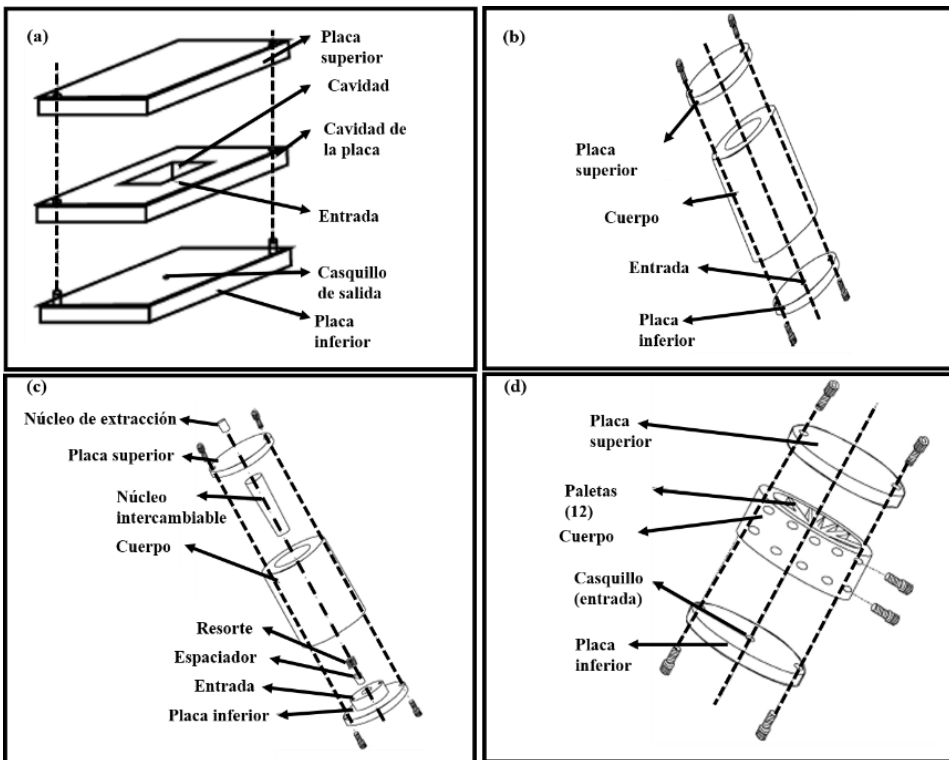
Moldes utilizados en el moldeo por inyección de polvos a baja presión, (a) molde para barras, (b) molde para cilindro, (c) molde para tubo y (d) molde para turbina [91].
